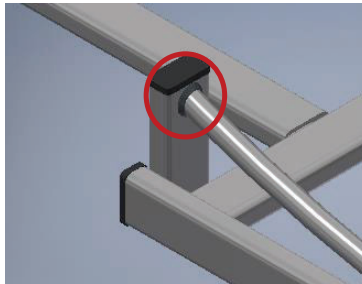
Ubicación de la soldadura corredera y soporte.
